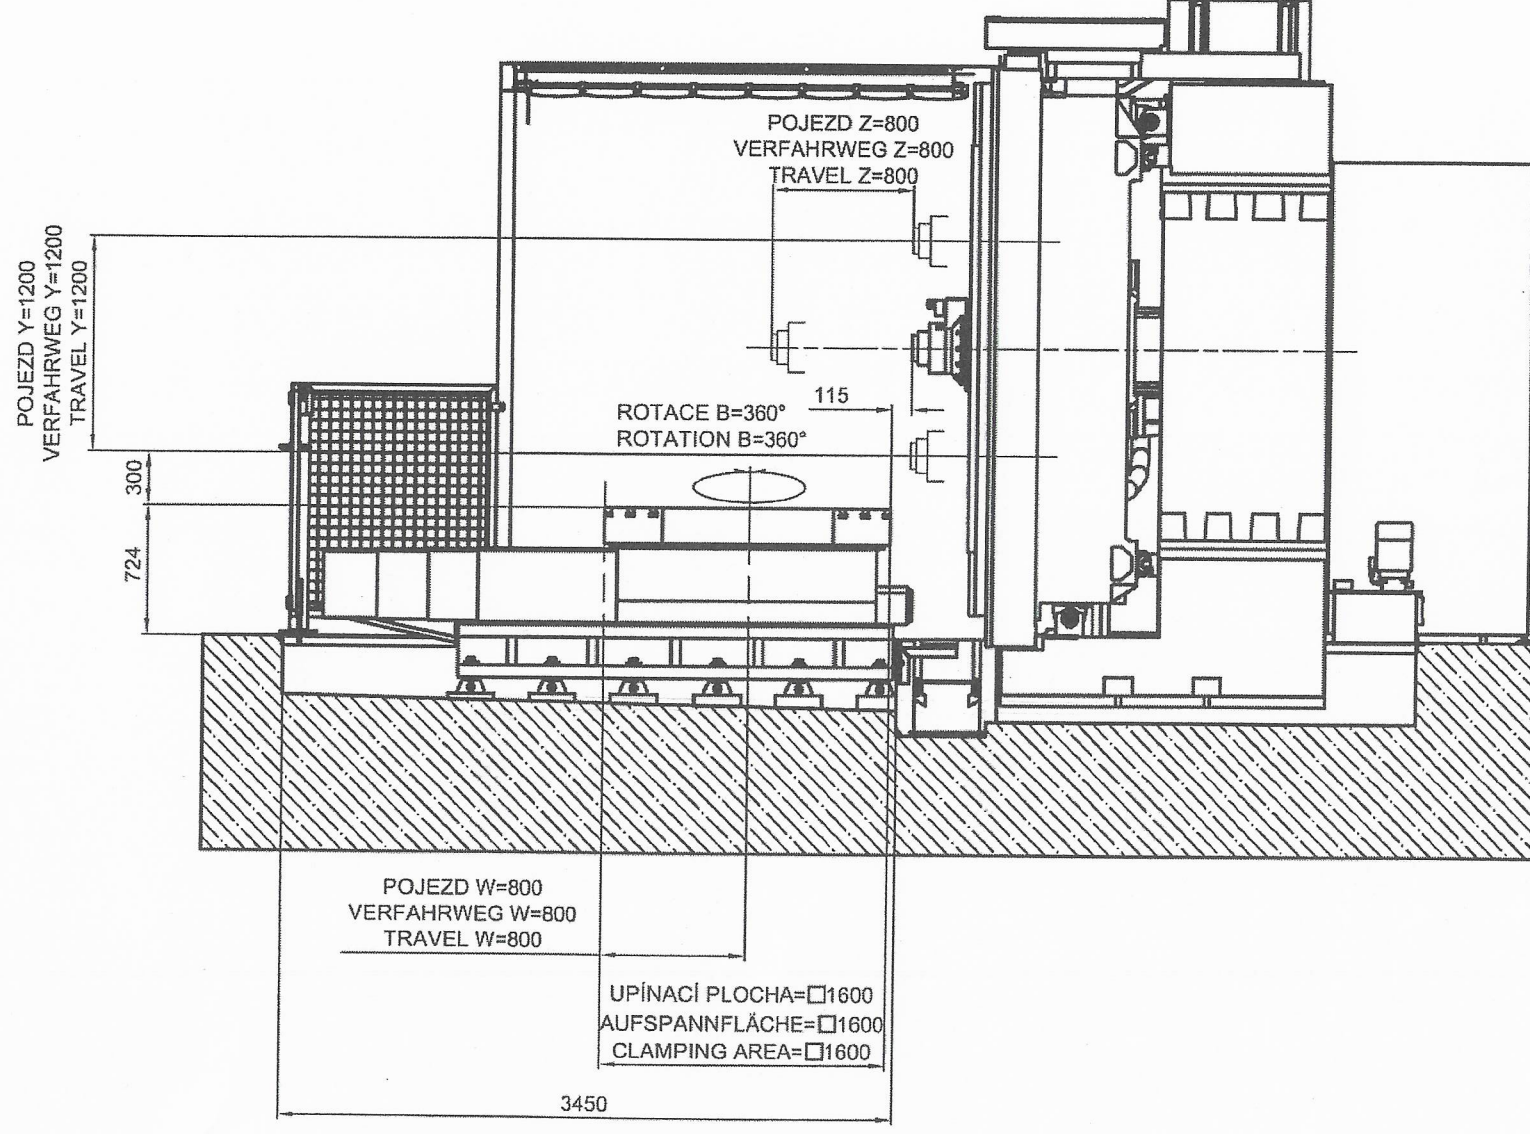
Bearbeitungsbereich der Maschine
